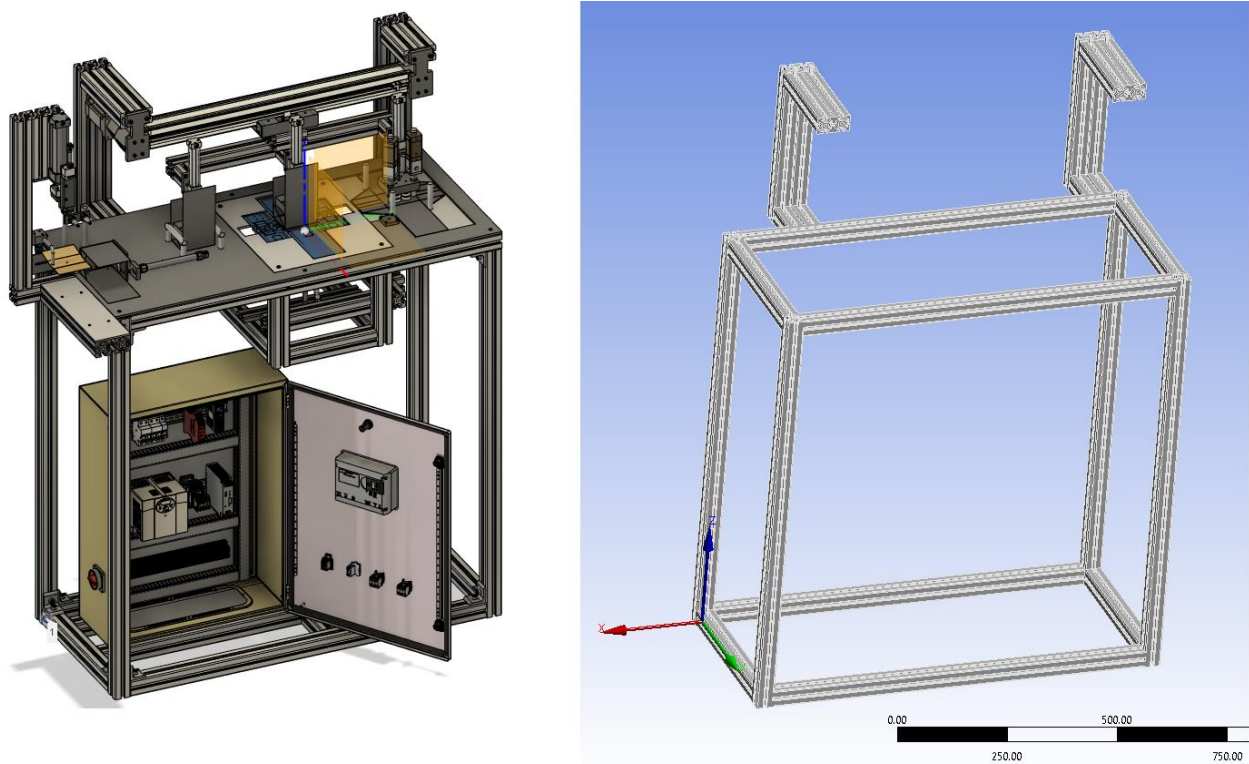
Máquina de doblaje de etiquetas y su origen en el diseño CAD.
